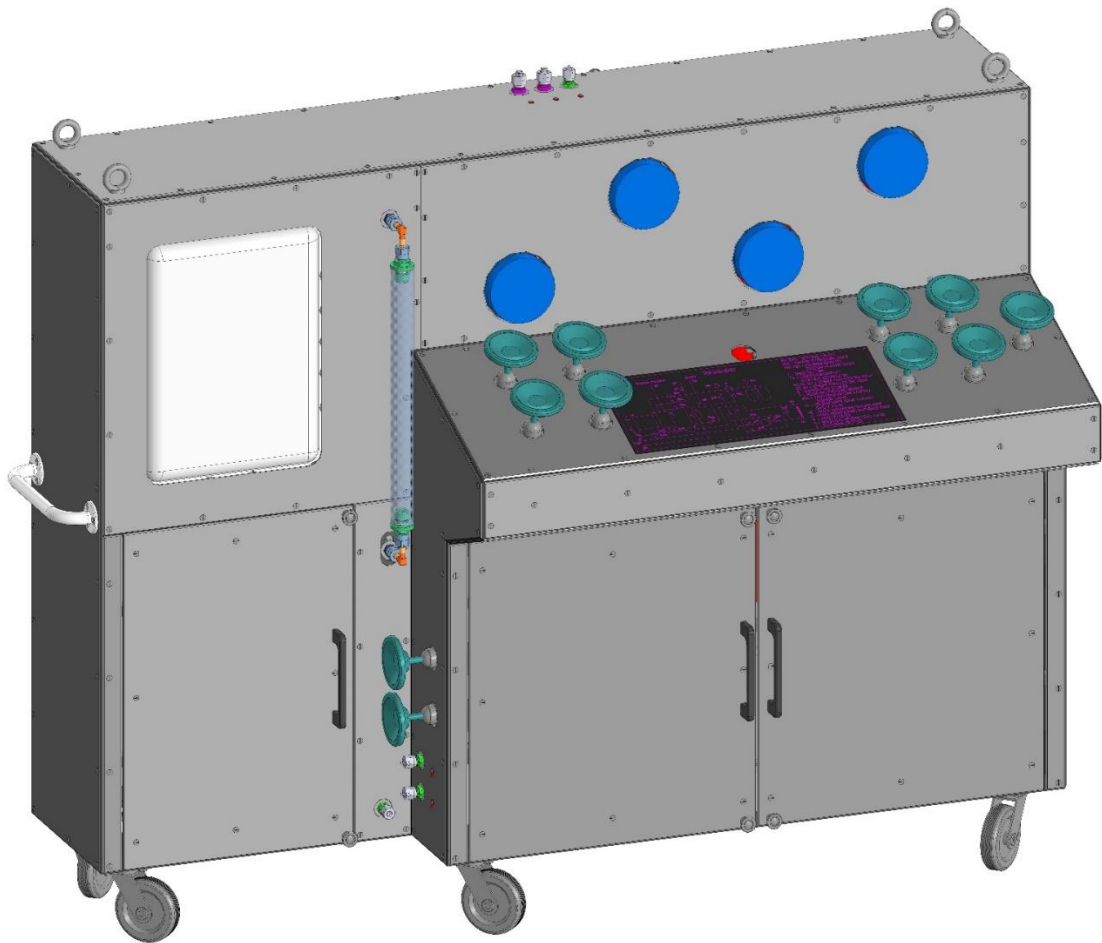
Внешний вид установки ДТО-95ТМ
